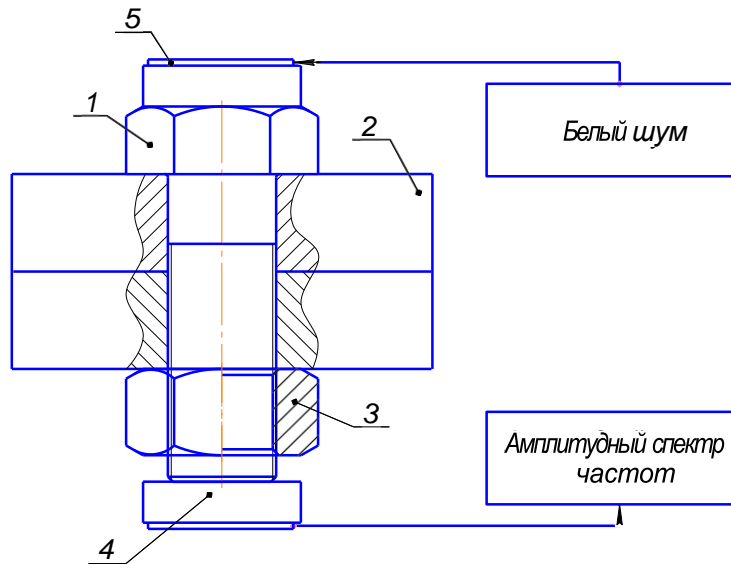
Теоретична схема контролю болтового з'єднання
